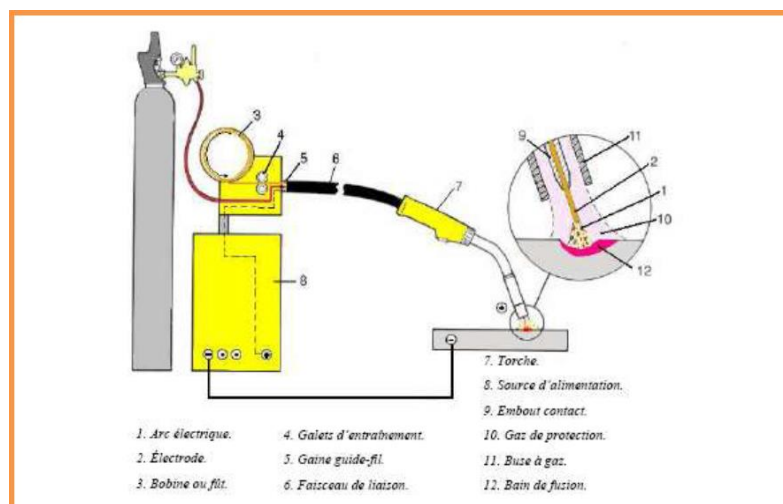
Principes du procédé de soudage MIG/MAG [18].
